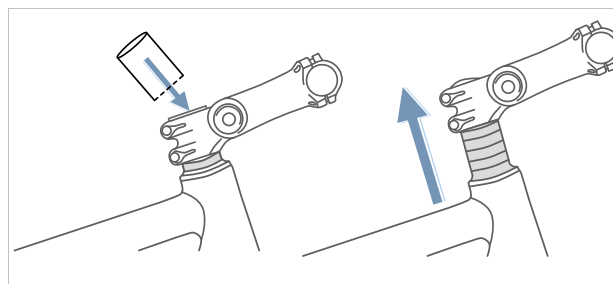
Ridicarea pipei Ahead prin montarea de inele distanțiere (Spacer)
